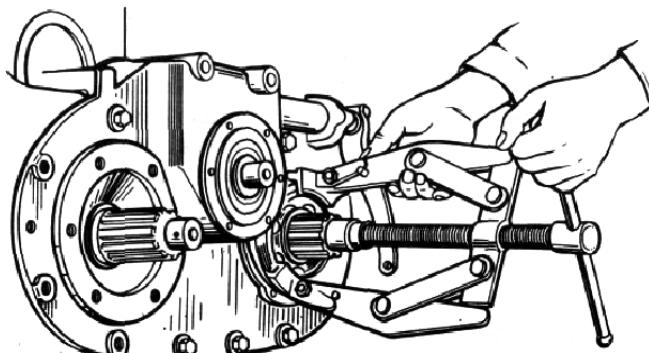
Выпрессовка подшипников вала промежуточного и заднего мостов
